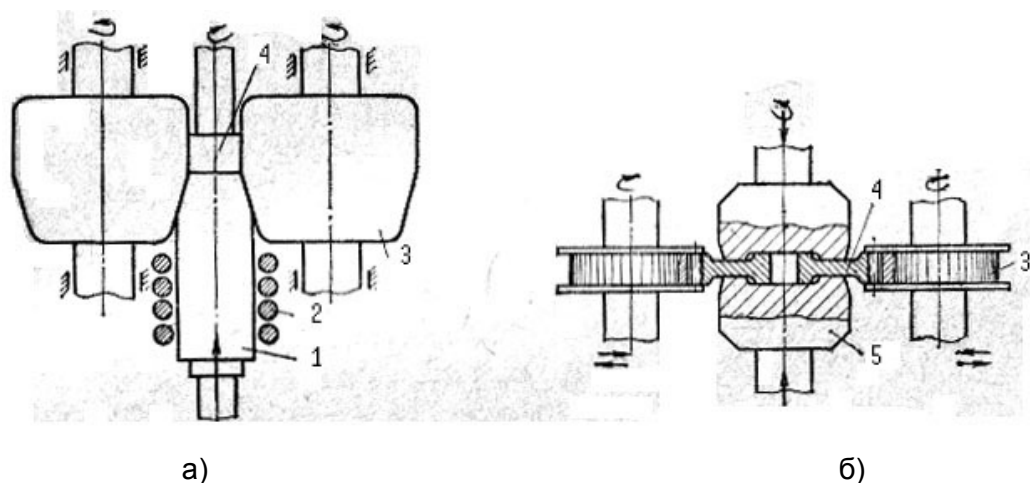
Схема накатки зубьев шестерен зубчатыми валками: а) при осевой подаче пакета заготовок; б) при радиальной подаче валков
